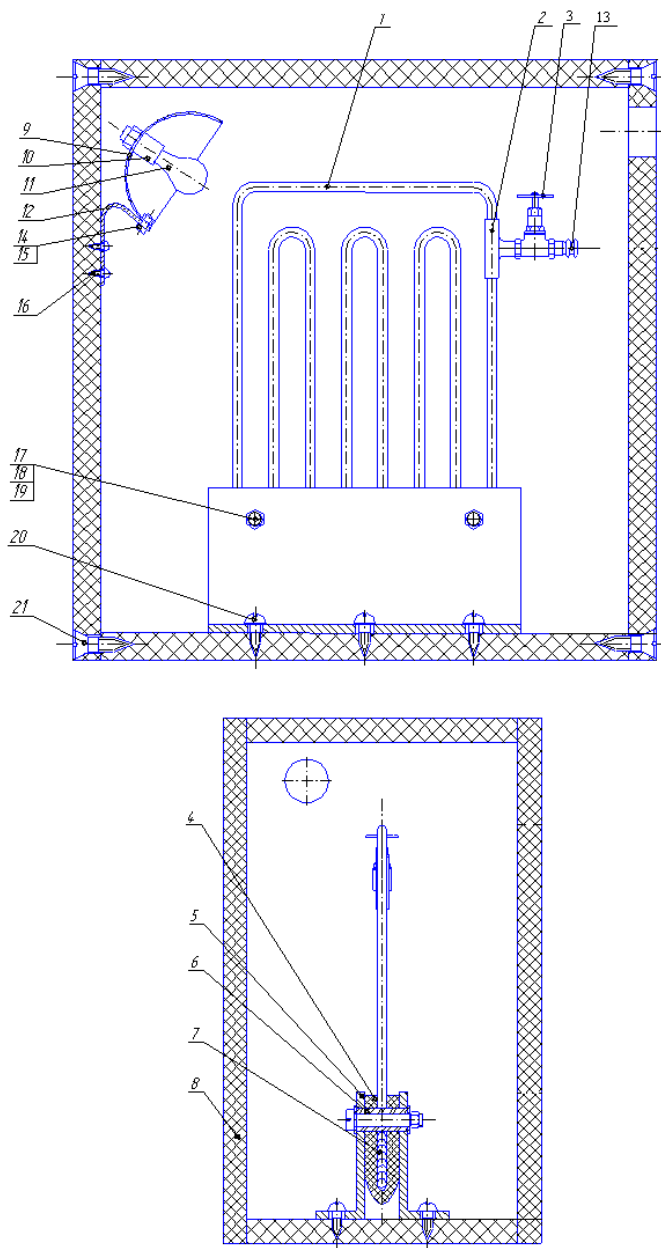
Бокс із розташованою в ньому скляною ПТТ: 1 - ПТТ; 2 - трійник; 3 – вакуумний кран; 4 - ізоляція; 5 - опорні ніжки; 6 - керамічна трубка; 7 - нагрівач; 8 – бокс; 9 - ламповий відбивач; 10 – патрон; 11 - лампа; 12 - металева пластинка; 13 – наконечник; 14,17 – гвинт; 15,18 – гайка; 16,20,21 – шуруп.
